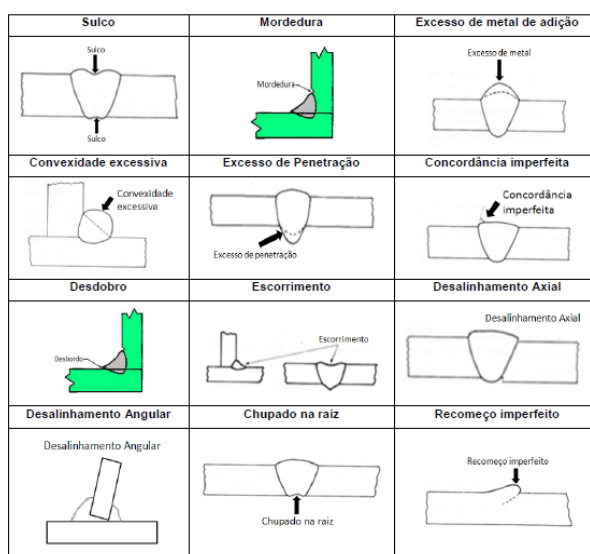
Defeitos de forma na soldadura [44].
